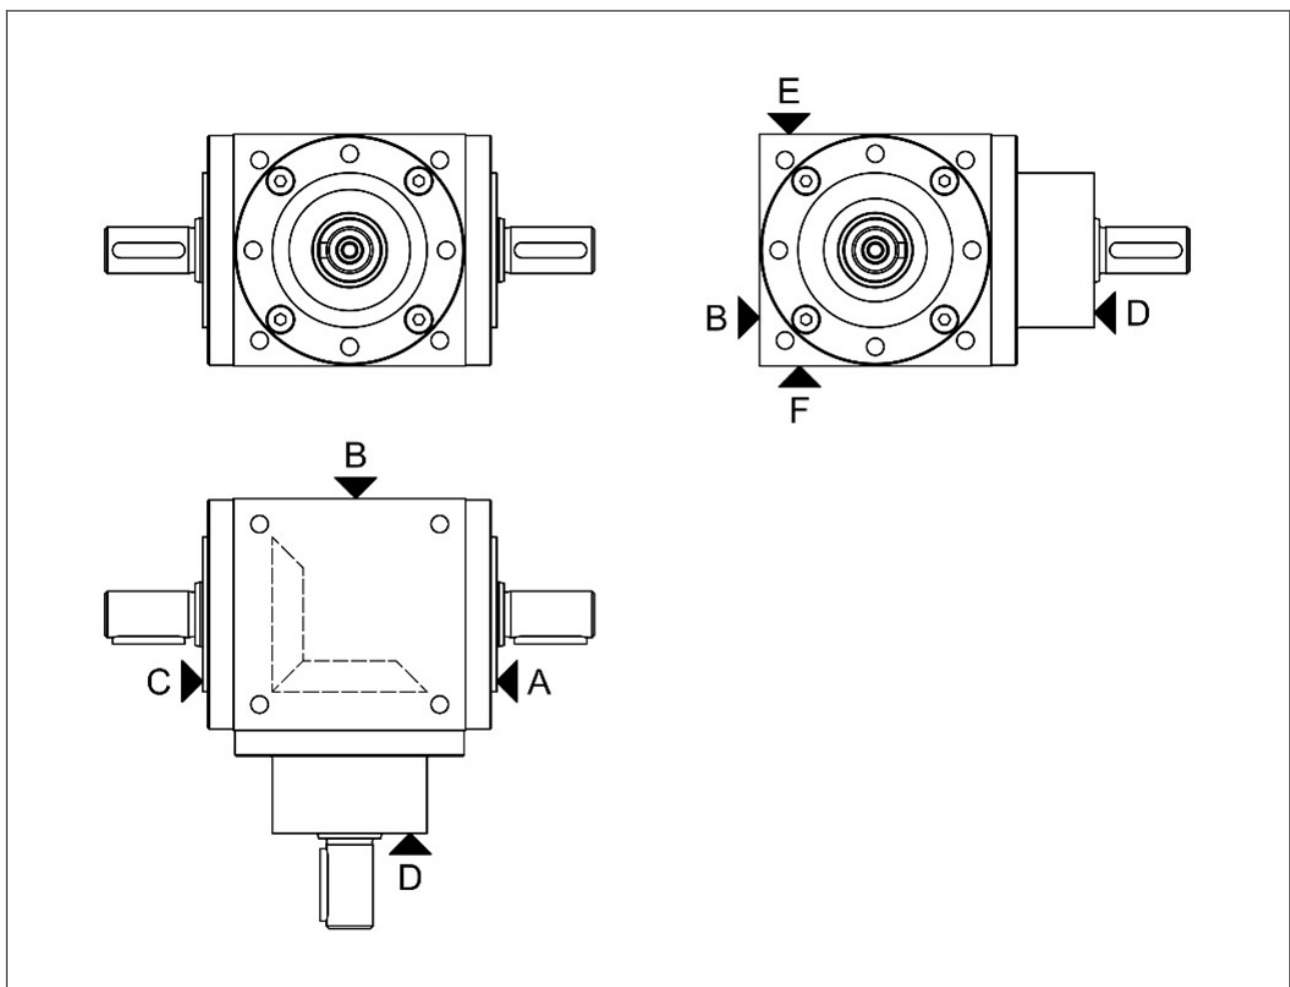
Vue d'ensemble du renvoi d'angle ZK ZIMM
